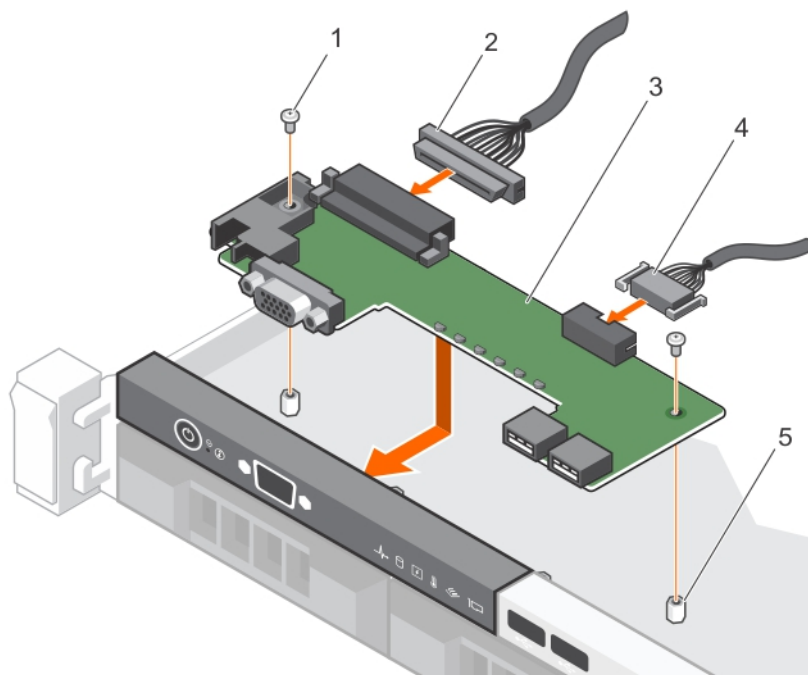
Installieren der LED-Bedienfeldplatine – Gehäuse für vier verkabelte Festplatten
